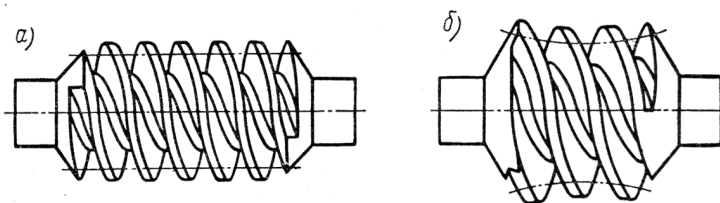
Виды червяков: а – цилиндрический; б – глобоидный.
